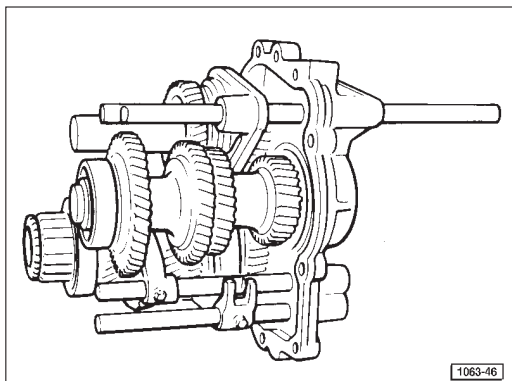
Ensemble des pignons de boîte de vitesses.
